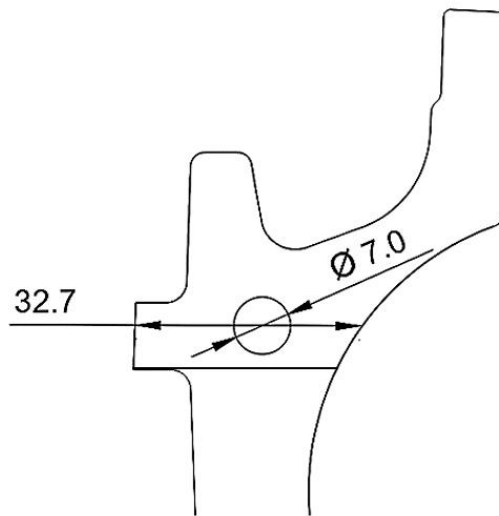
Dimensões (em mm) da secção de maquinagem do provete de tração.
